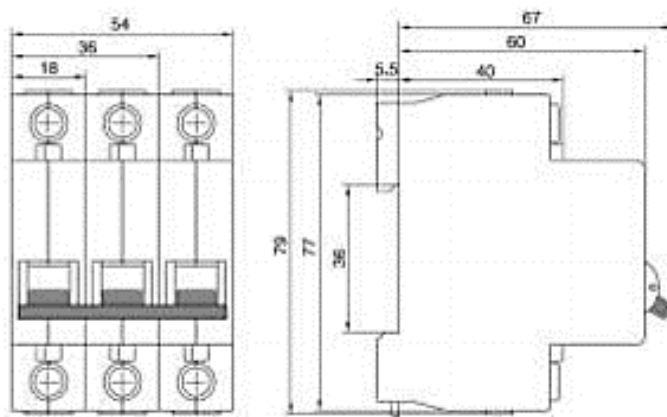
Dimensões Mini Disjuntor Termomagnético
